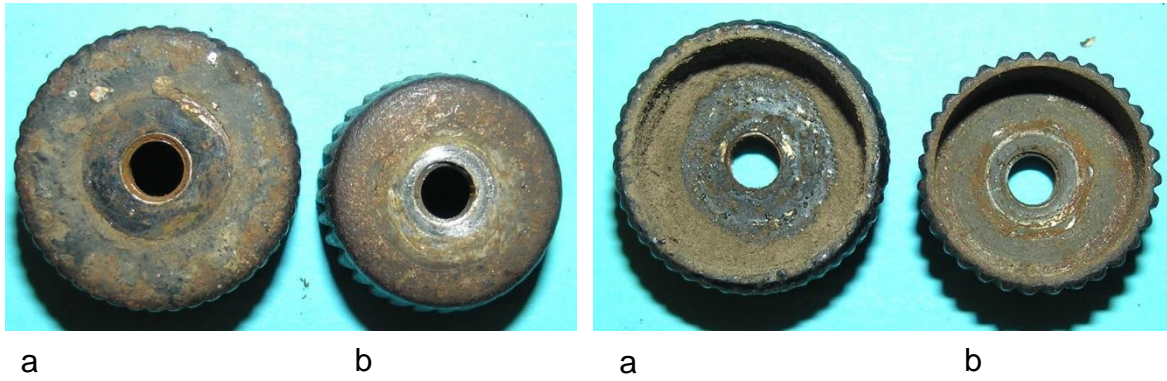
Reibräder mit Gewindebohrungen: a) Durchmesser 22 mm, b) Durchmesser 19 mm
